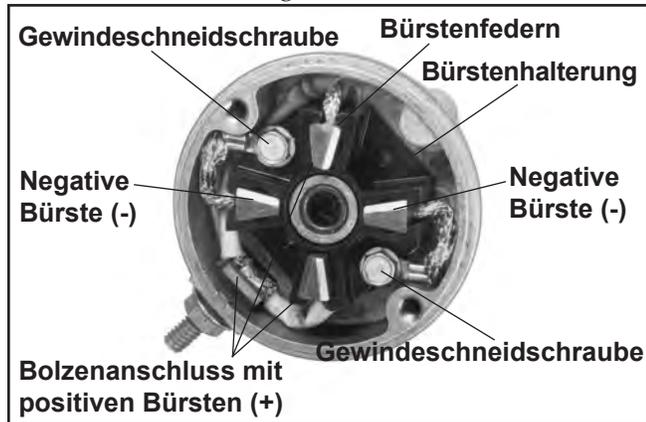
Endkappe Umschalter Typ "A" mit Bürsten.
